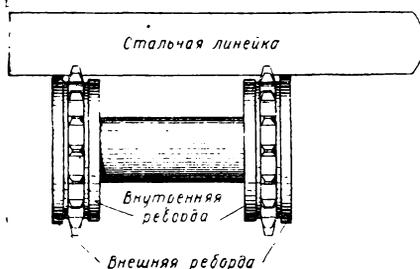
Проверка правильности изготовления реборд зубчатого барабана
